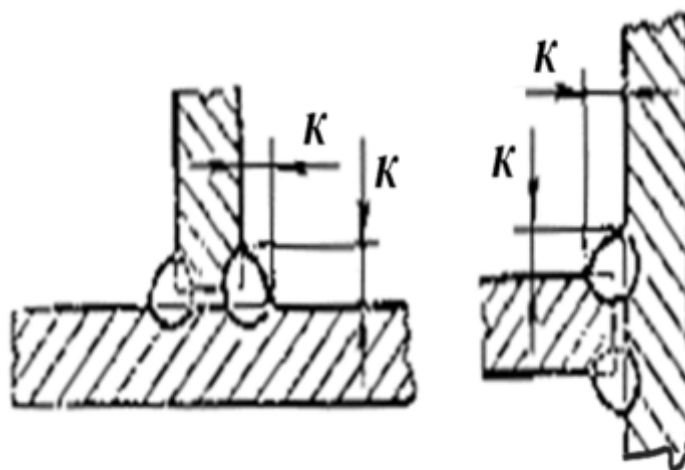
Схема сварного соединения ТЗ
